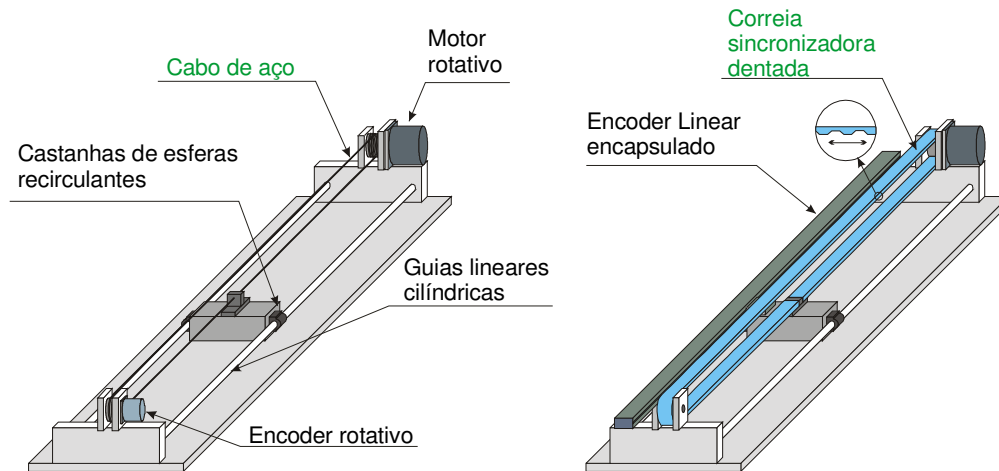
Módulos de transmissão a) Cabo de aço b) Correia sincronizadora dentada.
